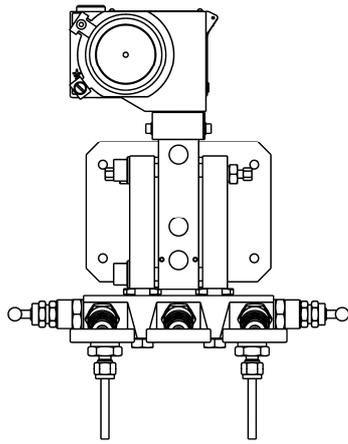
Шарнирный вентиляльный блок 1/2G в сборе
